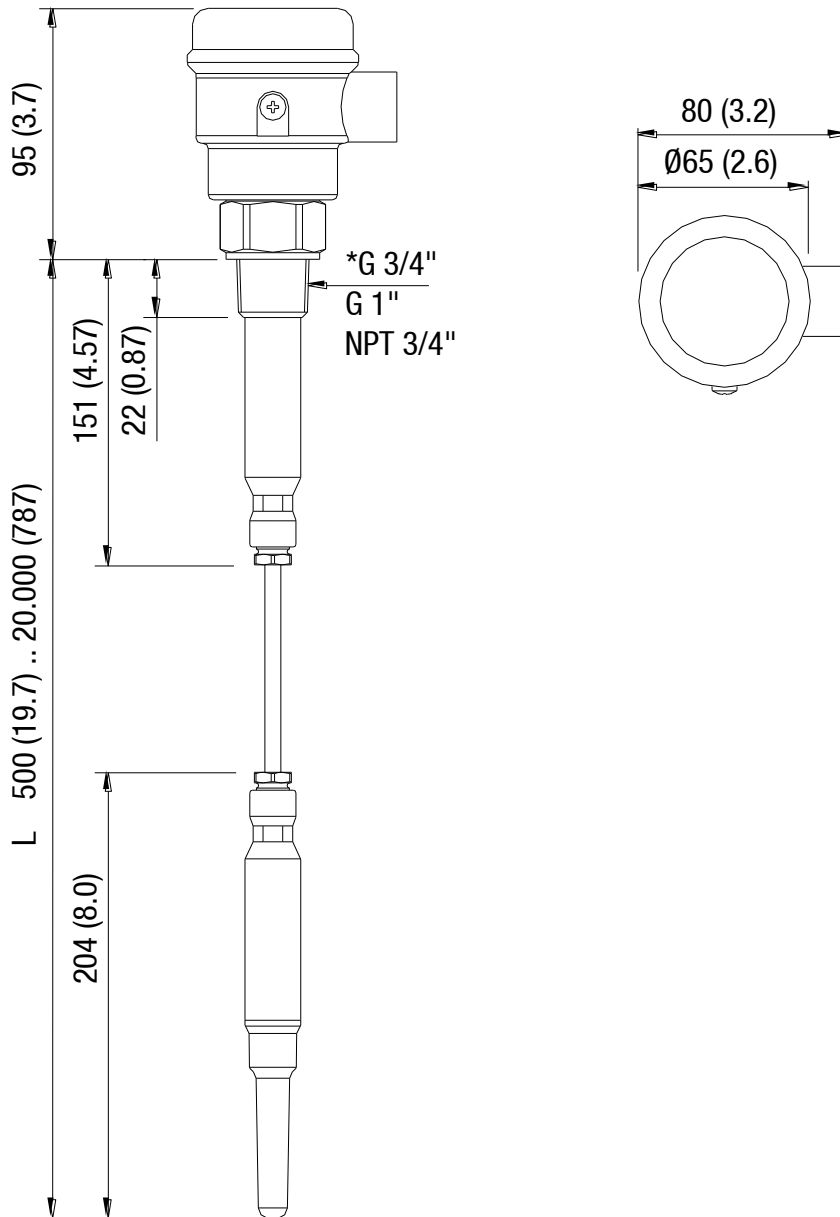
Abmessungen CN 7150, Gehäuse $\varnothing 65$ mm
